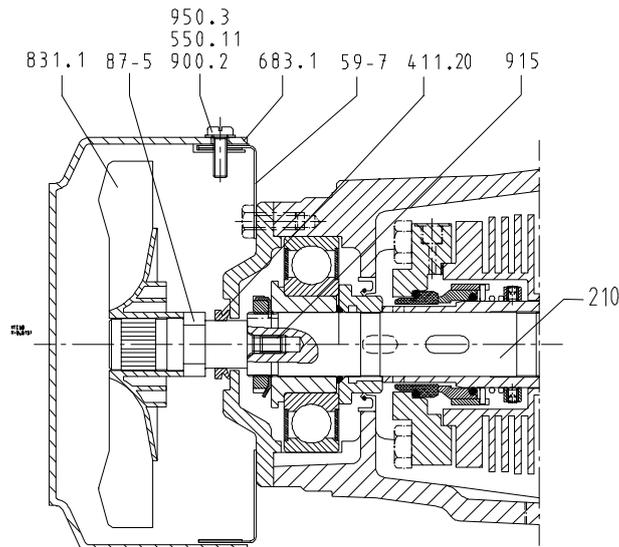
Desmontaje del cierre mecánico enfriado por aire: pasos adicionales de desmontaje
